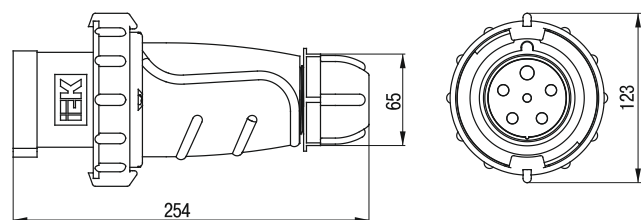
Габаритные размеры соединителей типа ССИ-033, ССИ-034, ССИ-035 / Figure 2 — Overall dimensions of
